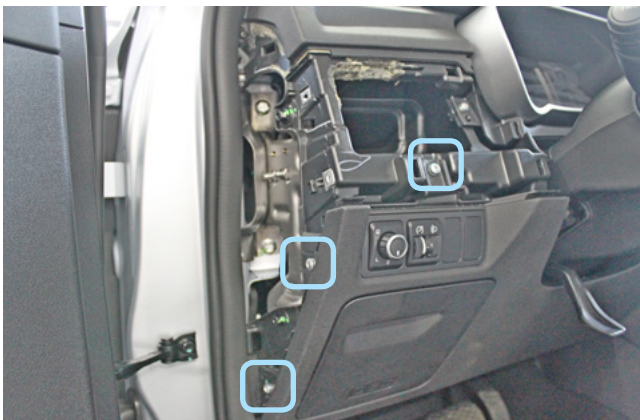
Саморезы крепления накладки под рулевой колонкой
